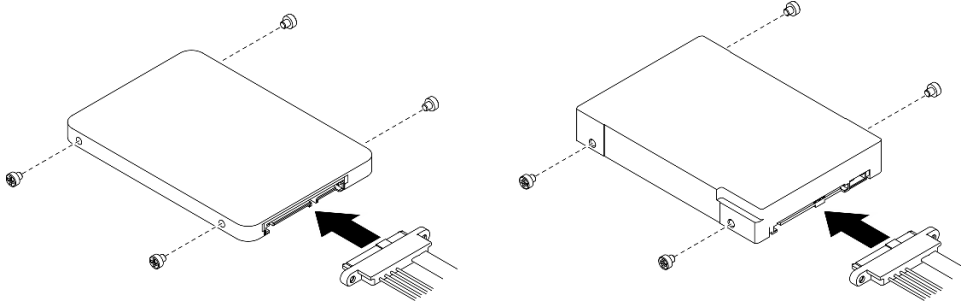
Instalación de tornillos y conexión de cables de la unidad
